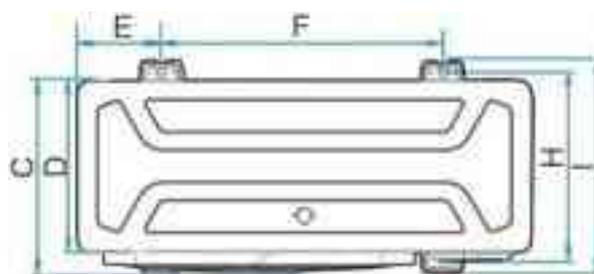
Dimensões da vista frontal do modelo 140/160 (unidade: mm)
